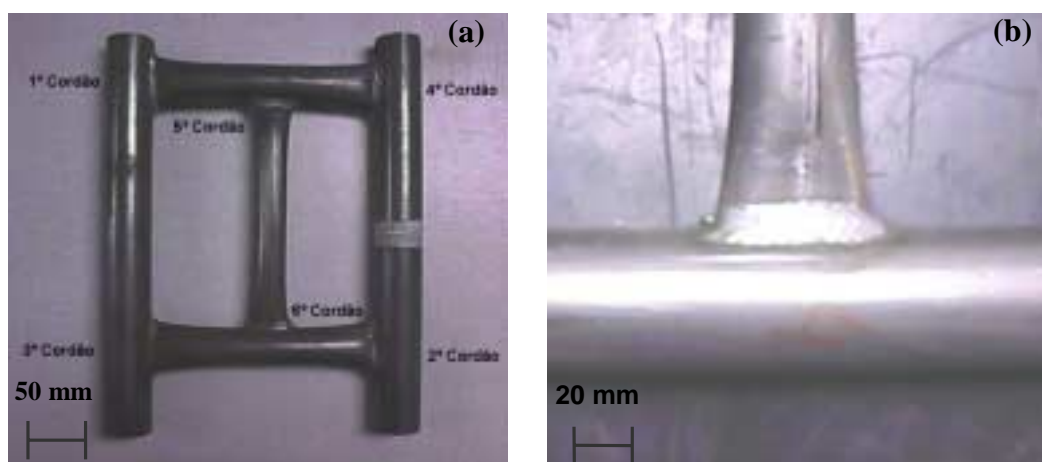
Em (a), uma seqüência de soldagem utilizando o robô e em (b), o aspecto visual da solda obtida pelo processo robotizado.
